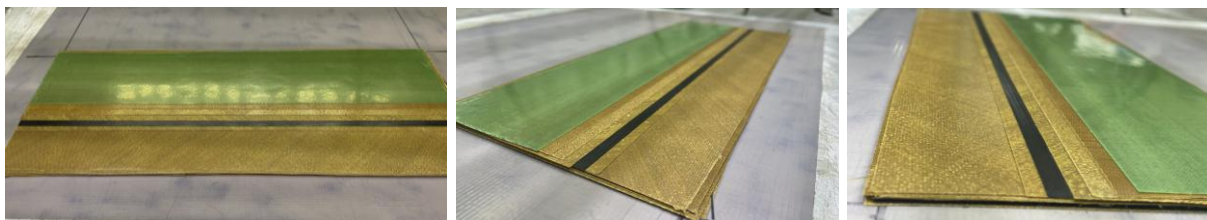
Общий вид пакета-заготовки конструктивно-подобного образца гибкого элемента
